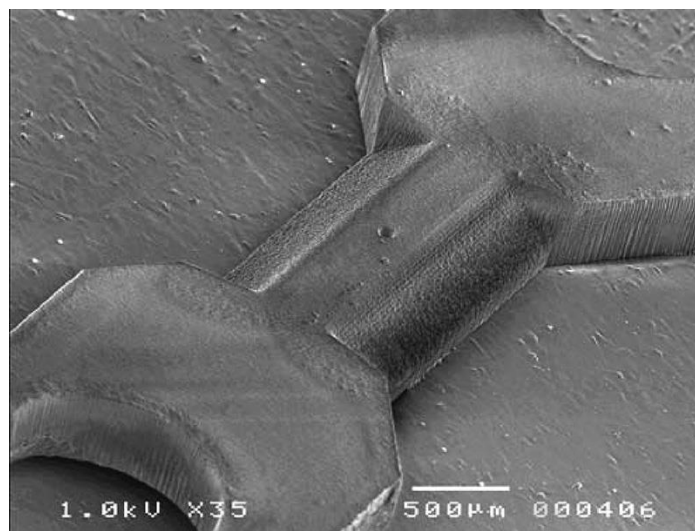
Деталь, демонстрирующая возможности лазерного сверления и фрезерования
